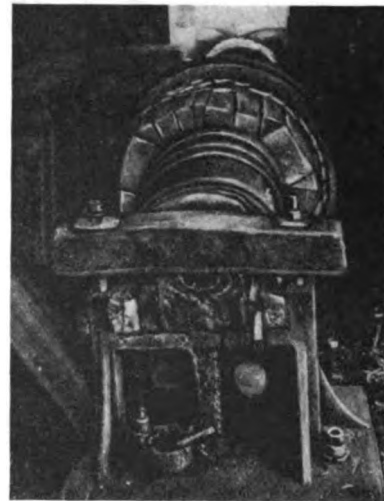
Lagerung der Wasserradwelle des Hammerwerks Ernstthal b. Oliva (17. Jahrh.)
